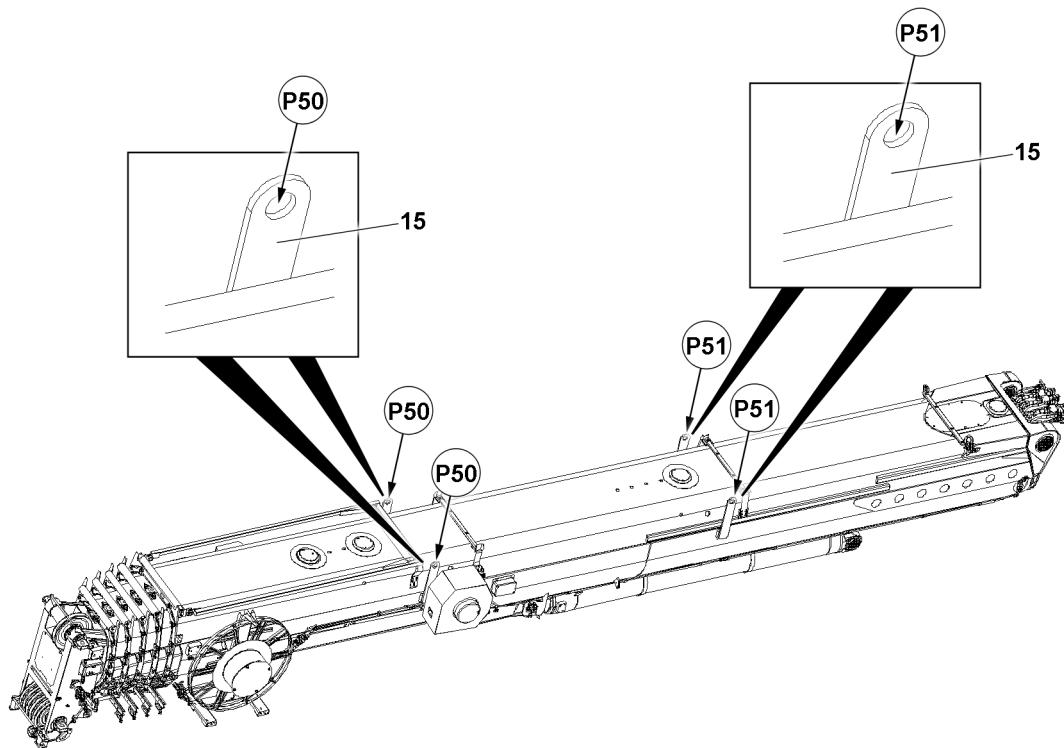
Elevar la pluma telescópica con dispositivo de elevación
